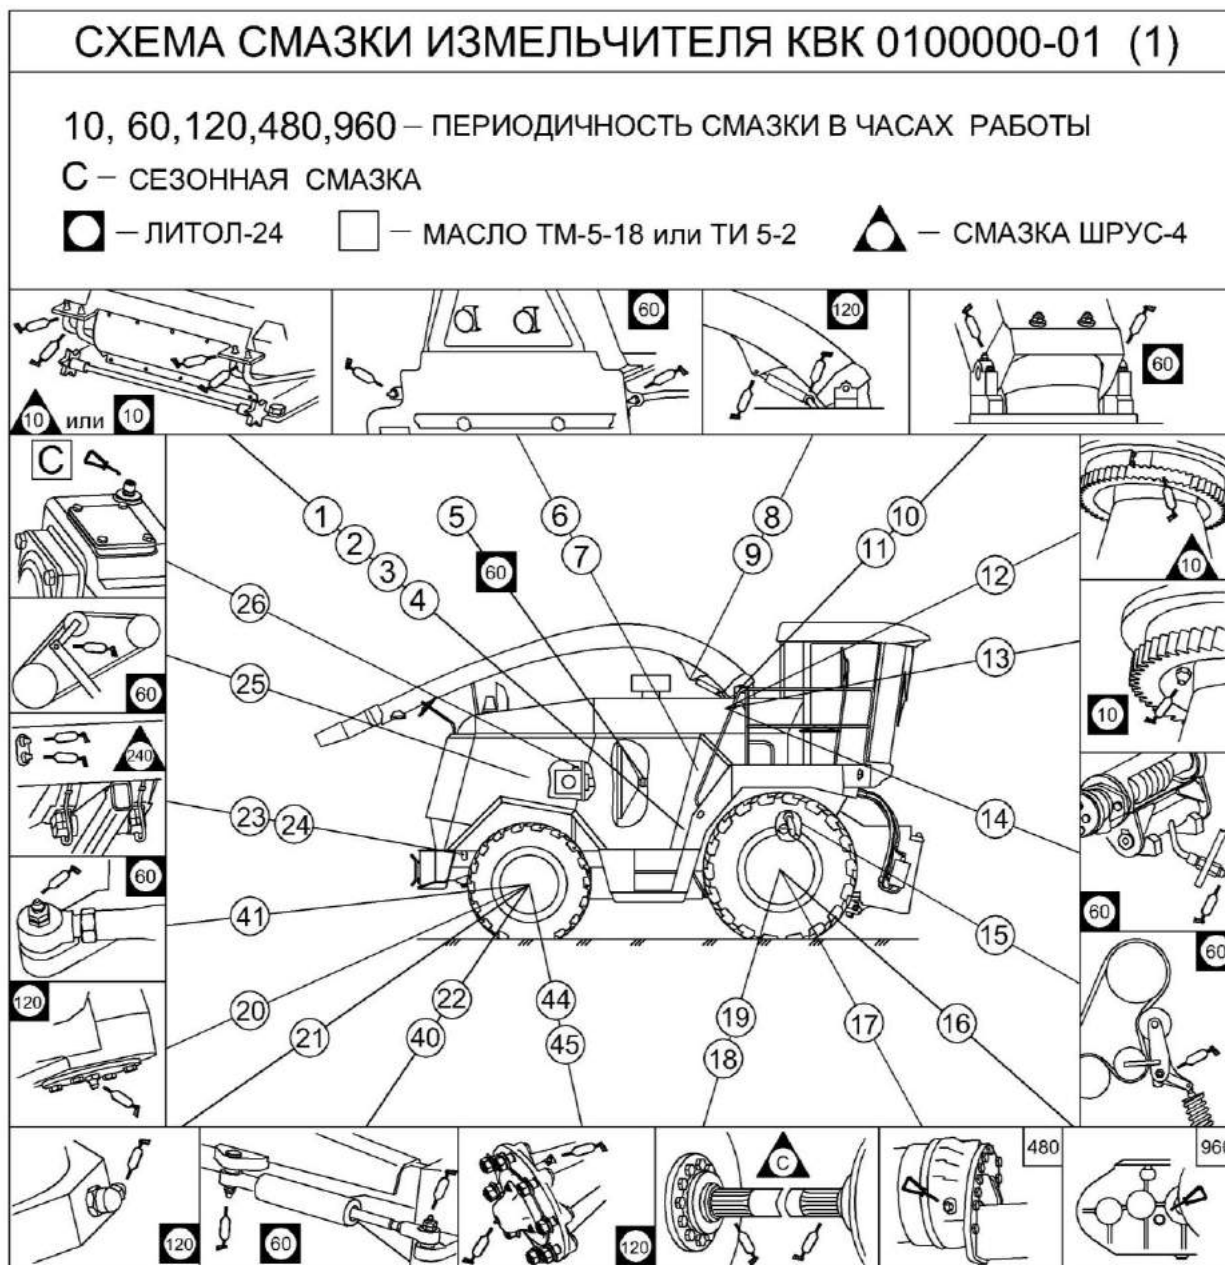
Схема смазки измельчителя КВК 0100000-01 (вид справа)
